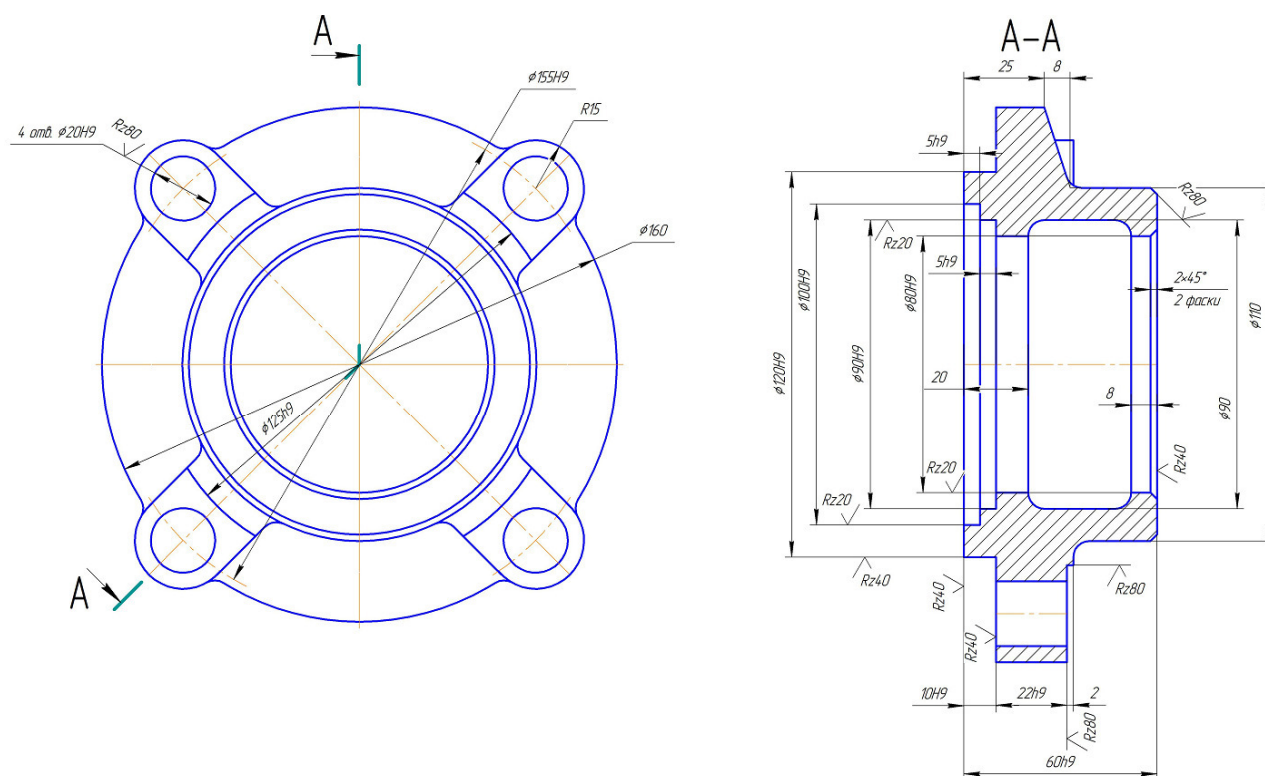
Эскиз детали «Крышка подшипника задняя»
